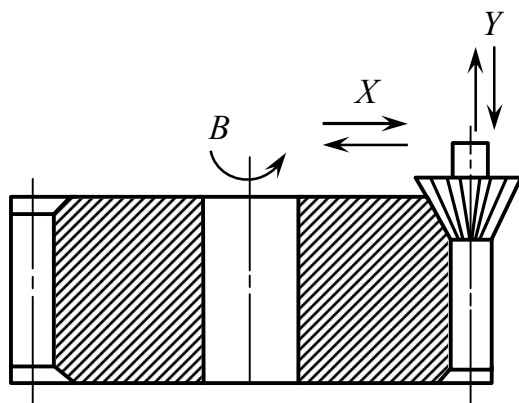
Схема фрезерования фасок на станке с ЧПУ
